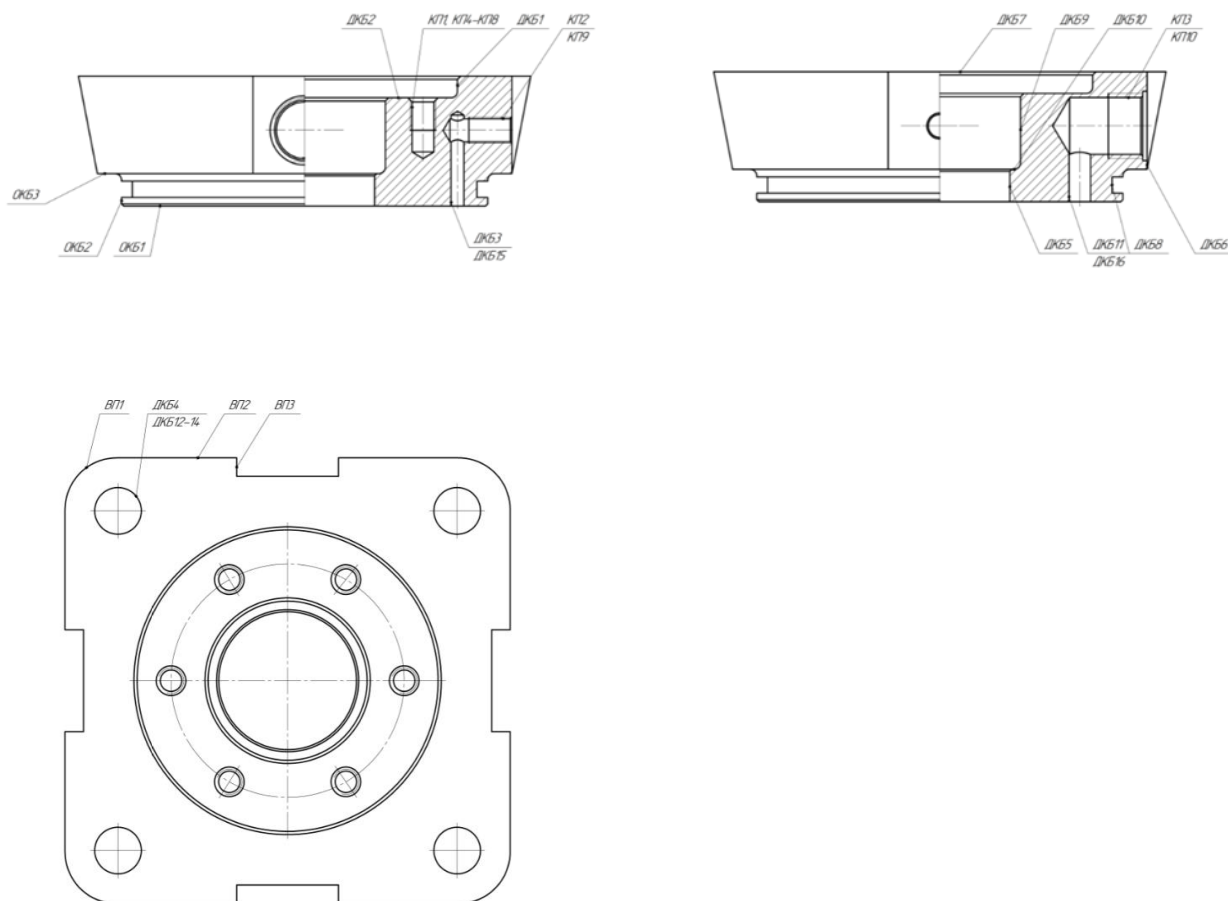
Класифікування поверхонь деталі «Корпус»
